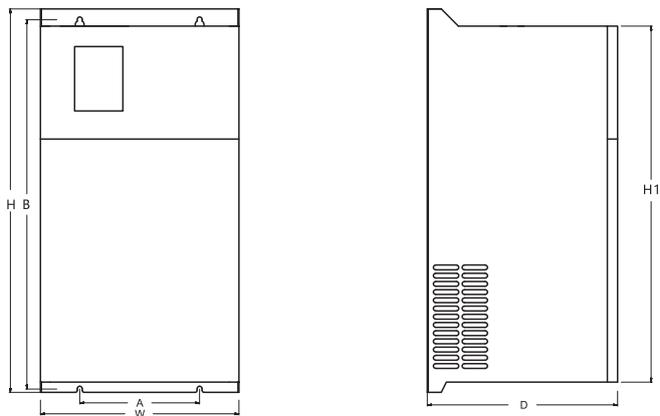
FU9000D系列 钣金结构外型尺寸及安装尺寸示意图
